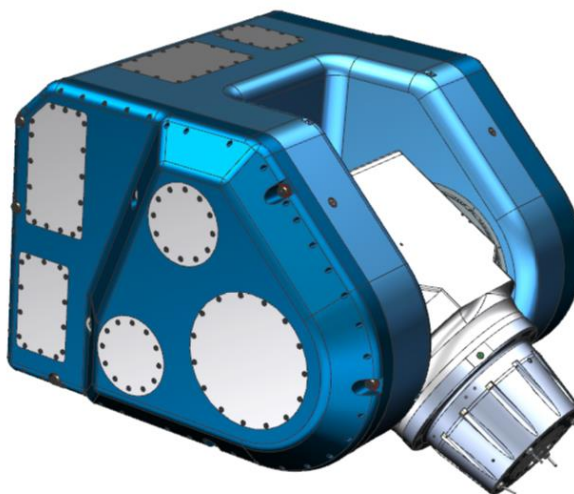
Boční pohled na upořáání komponentu ve frézovací hlavě
